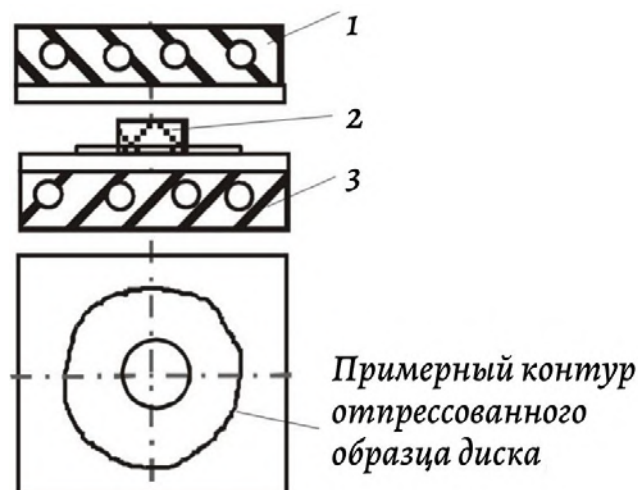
Пресс-форма для прессования образцов-дисков:
